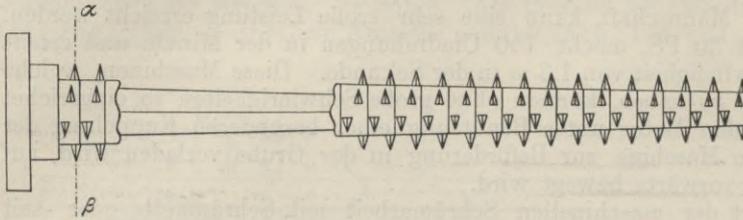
Fräse der Goolden-Atkinson-Maschine.
